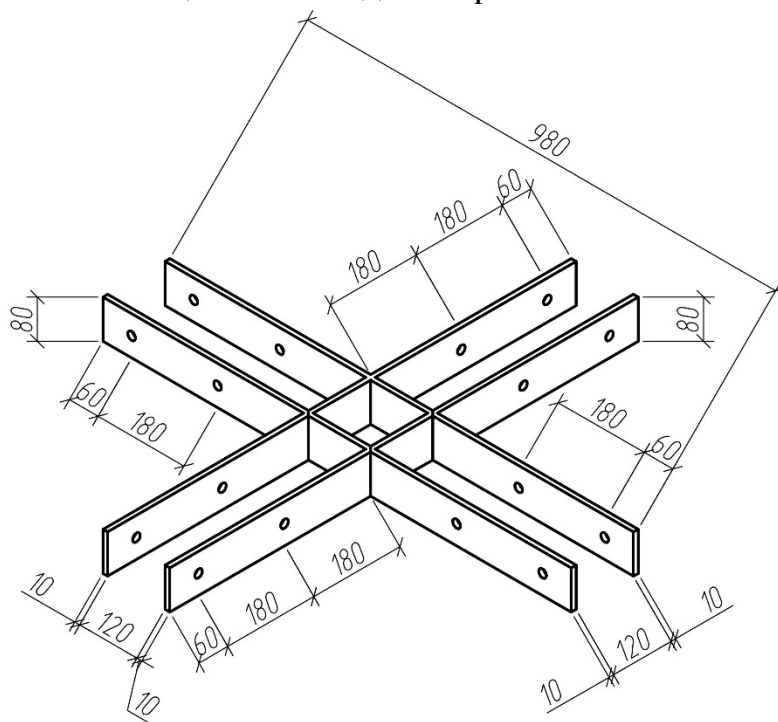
Соединительный сварной элемент СЭ-1в (СЭ-1н)
